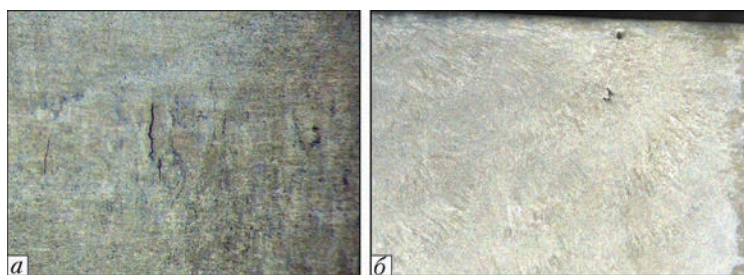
Дефекты в сварном шве: а – микротрещины; б – поры толще металла и не имеющие выхода на поверхность, в большинстве случаев представляют собой поры диаметром около 1 мм и трещины длиной 1...5 мм (рис. 2) [2].
